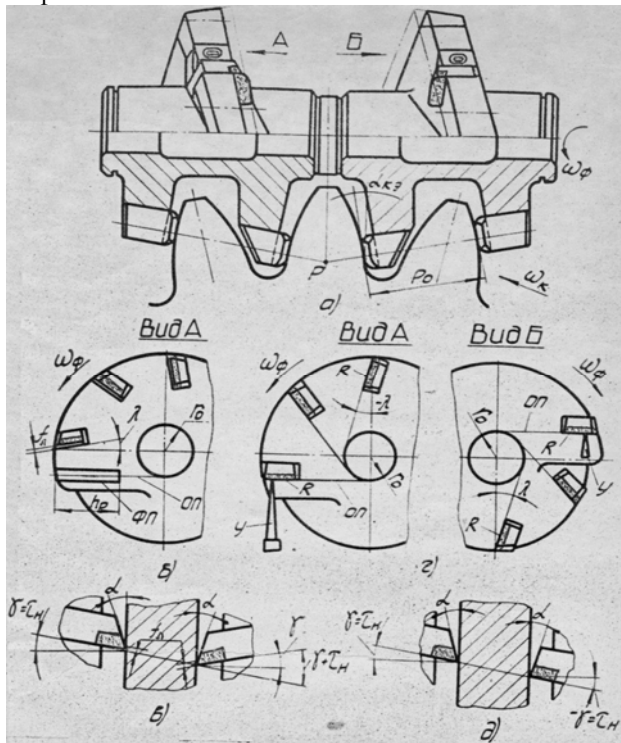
Профилирование специальных фрез на основе эвольвентного червяка: а – схема обработки зубьев колеса корпусами фрезы; б – расположение зубьев фрезы с винтовой ленточкой; в – геометрия режущей части фрезы при наличии винтовой ленточки; г – расположение зубьев фрезы в плоскостях, касательных к основному цилиндру; д – геометрия режущей части фрезы без винтовой ленточки.
